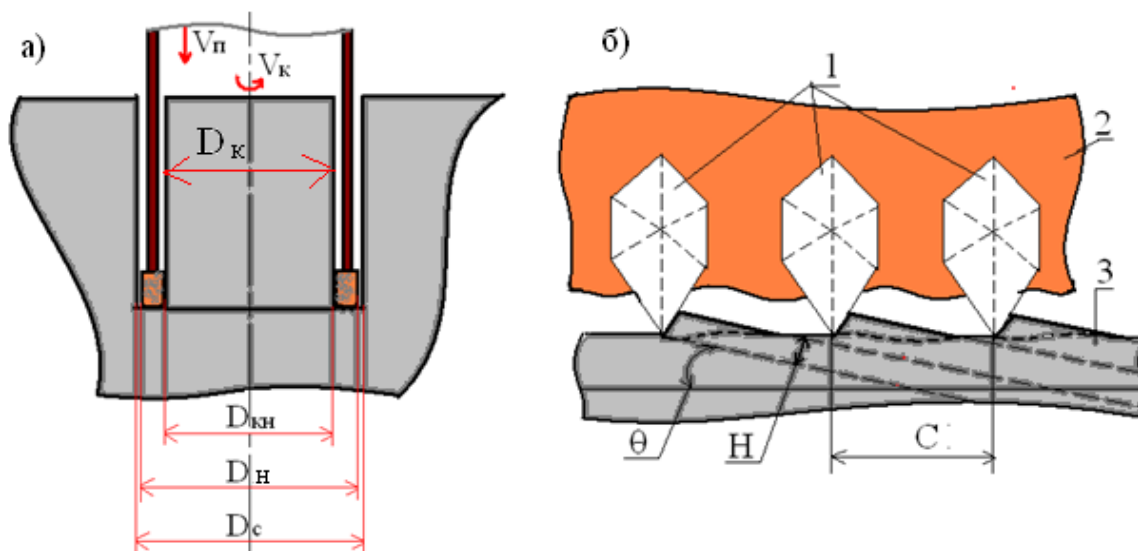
Схема движения алмазных зерен при кольцевом алмазном сверлении: а) – положение кольцевого алмазного сверла в камне (скважине); б) – развертка и схема движения алмазных зерен по винтовым линиям; 1 – алмазные зёрна; 2 –связка алмазного инструмента; 3 –декоративный камень.
